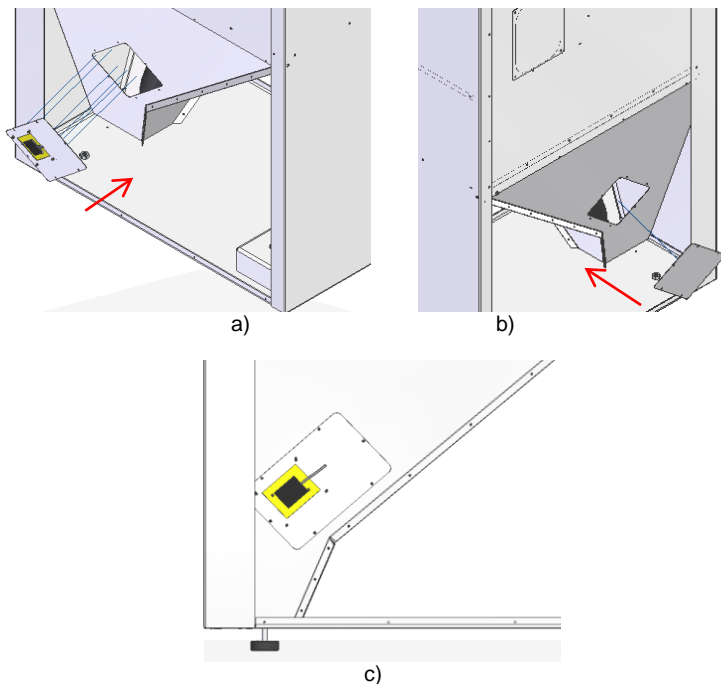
Colocación del sensor de nivel de pellets en el silo (instalación a la izquierda de la caldera)
